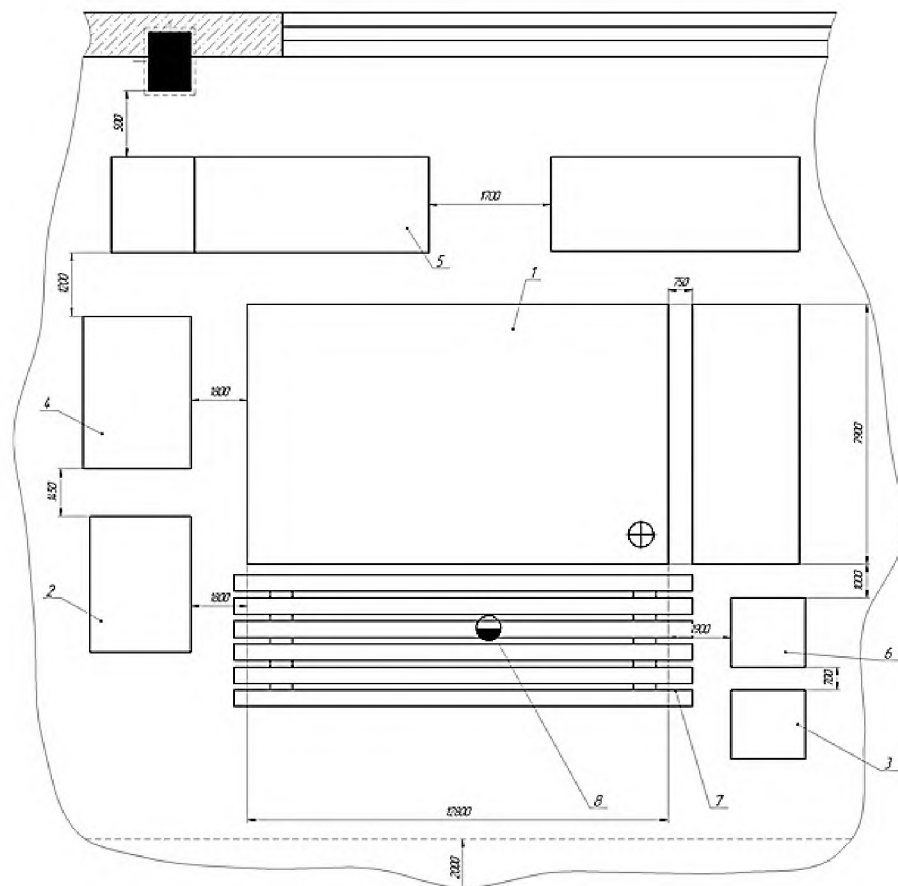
Планування робочого місця для горизонтального фрезерно-розточувального верстата: 1 – верстат мод. TOS VARNSDORF WHN 13 CNC; 2 – столик прийомний; 3 – тара для заготовок; 4 – тумбочка інструментальна; 5 – стелаж для пристосувань; 6 – тара для готових деталей; 7 – ґрати під ноги; 8 – верстатник
